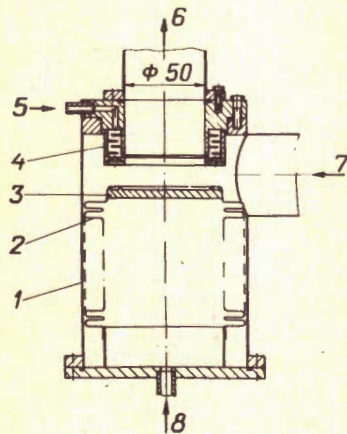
Предохранительный клапан. 1 - корпус, 2 - сильфон, 3 - золотник, 4 - седло с резиновой прокладкой и радиатором, 5 - обогрев седла, 6 - обратный поток, 7 - патрубок криостата, 8 - удерживающее давление.
